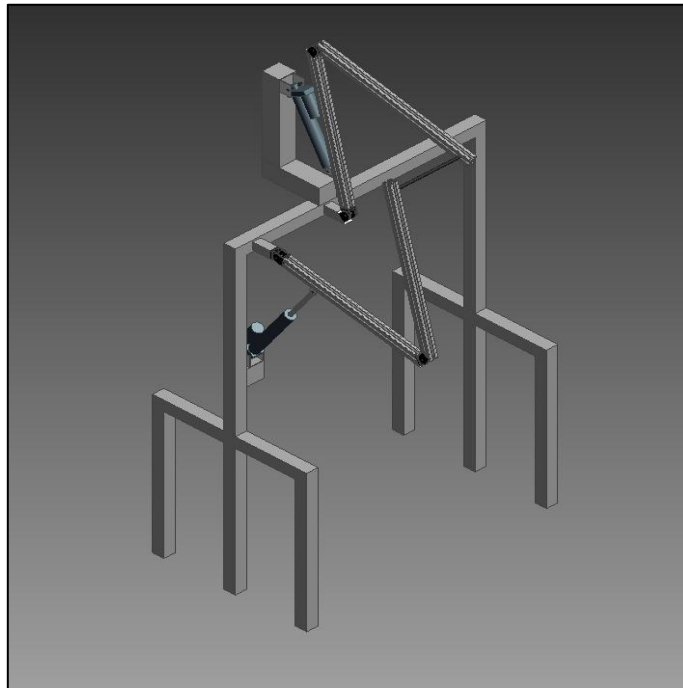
Dibujo CAD del mecanismo con el efector final hacia arriba.
